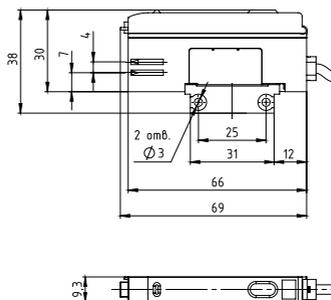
Габаритные и установочные размеры усилителей OF65-UR000FN3.U5.K.D / OF65-UR000FP3.U5.K.D
